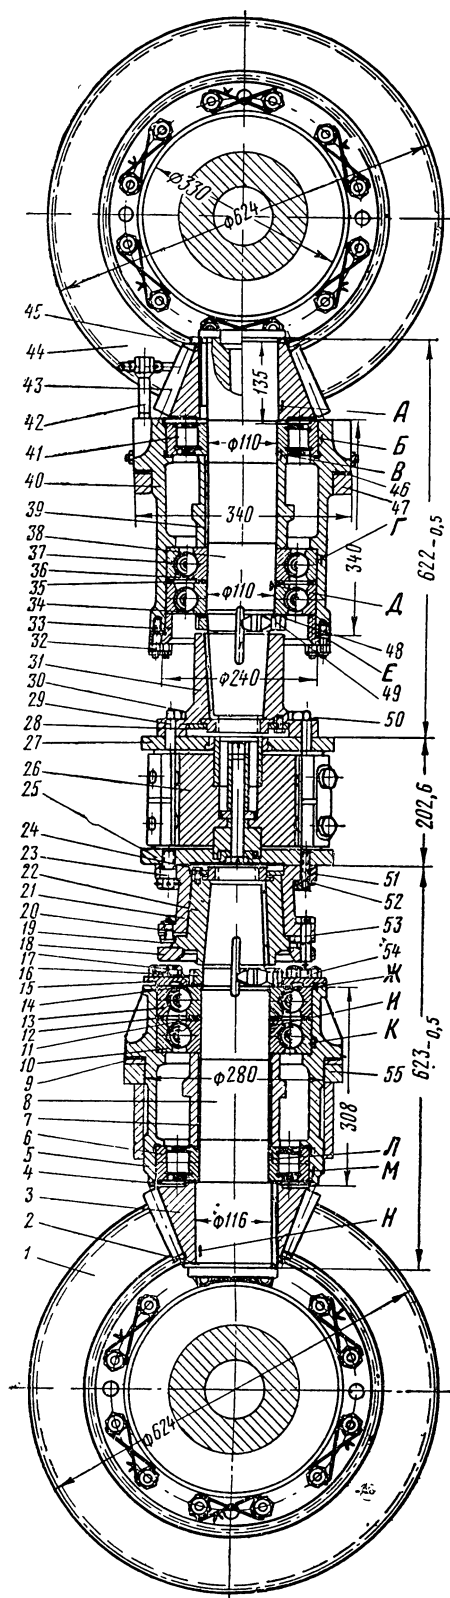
Верхний корпус вертикальной передачи (обозначения см. на рис. 33 и 35). Внизу показано соединение контрольного зуба стопорной планки с конусной муфтой
